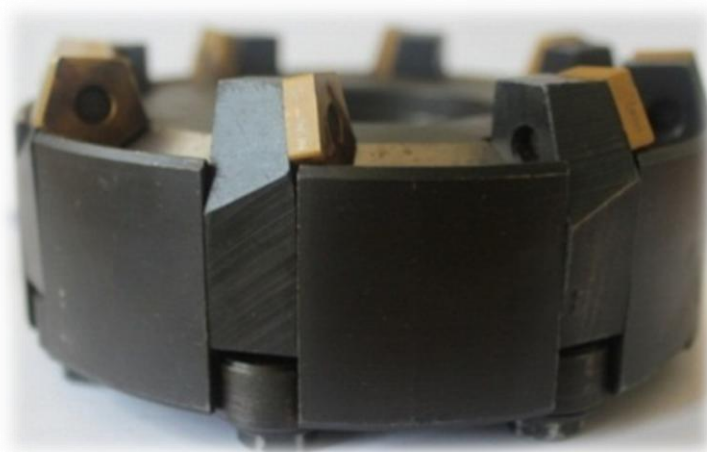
Торцовая фреза конструкции ВНИИ инструмента
